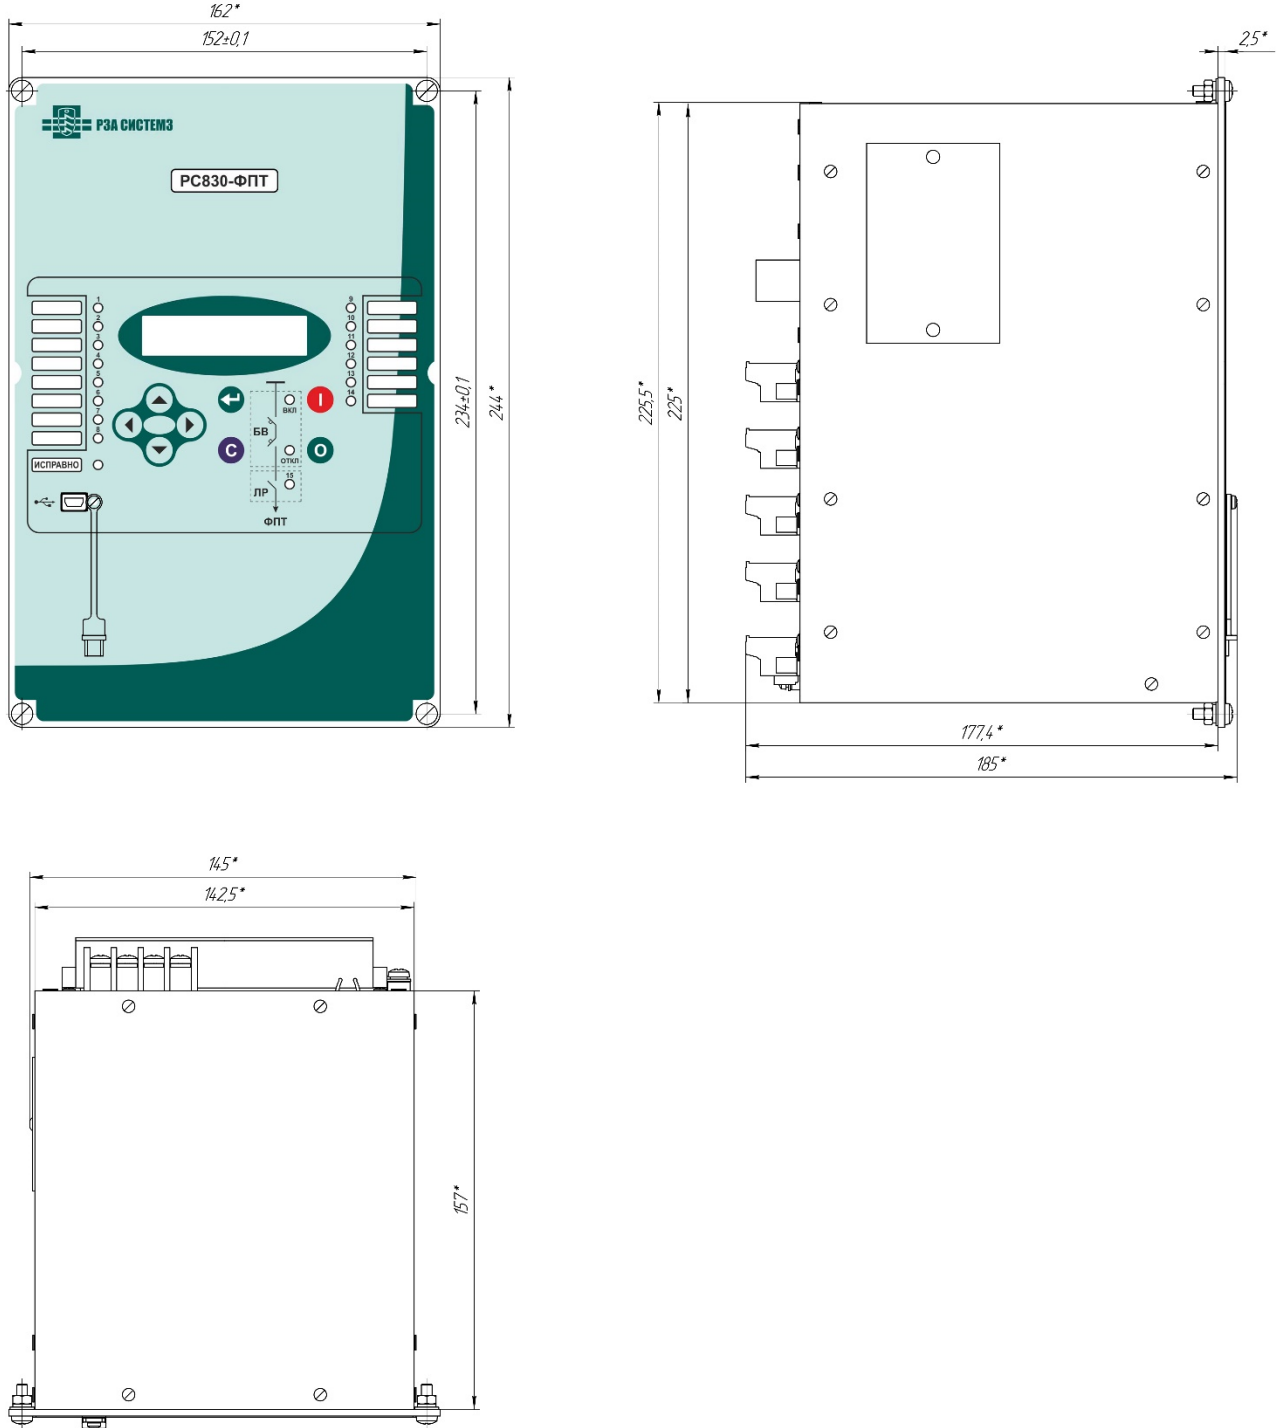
Габаритные и присоединительные размеры релейного блока РС830-ФПТ
